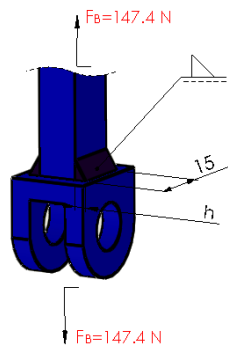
Diseño de la soldadura en la biela.
